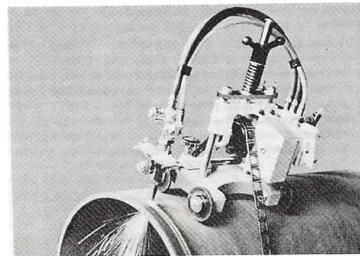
Machine portable pour l'usinage des tubes.
